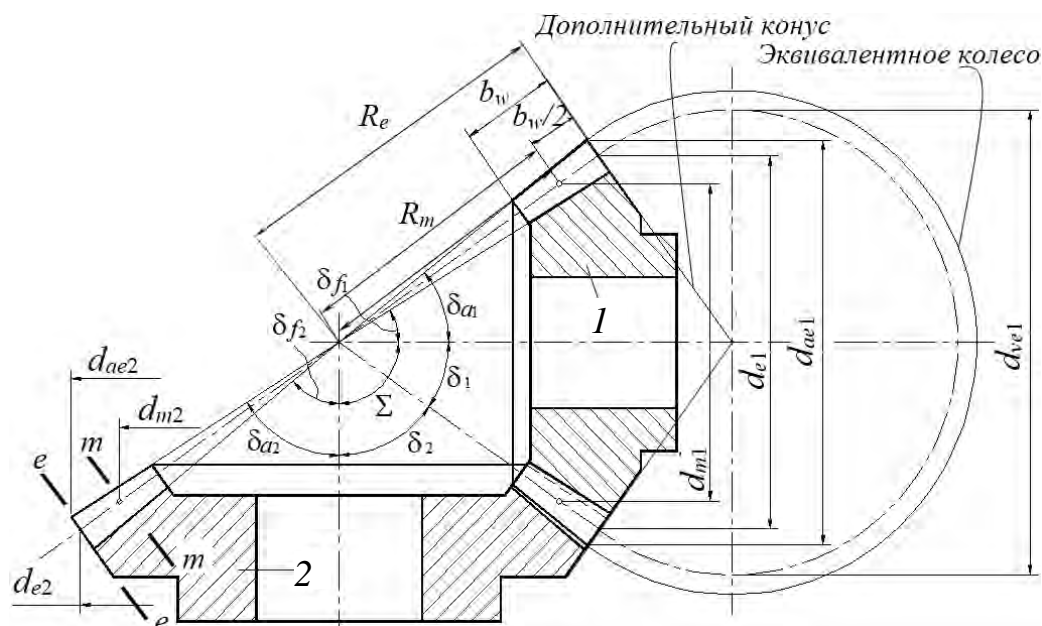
Схема конической передачи: 1 – шестерня; 2 – колесо
